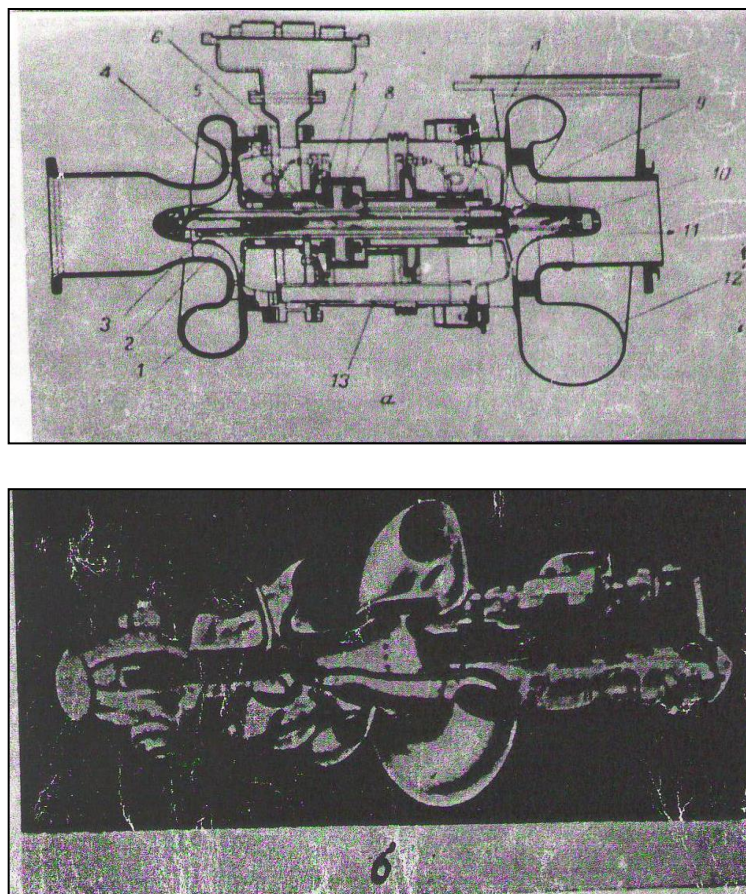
Снабженные газовыми подшипниками турбокомпрессор и турбогенератор электрической мощностью 8,5 КВт; а – турбокомпрессор, разработанный фирмой AiResearch (1-выходной патрубок компрессора; 2 – компрессор; 3 – медные втулки; 4 – радиальный подшипник; 5 – узел упорного подшипника; 6 – приборный блок; 7 – неподвижные поверхности трения упорного подшипника; 8 – вращающийся диск упорного подшипника; 9 – турбина; 10 – стягивающая шпилька; 11 – выход из турбины; 12 – входной патрубок турбины; 13 – каркас; б – турбокомпрессор и турбогенератор.
